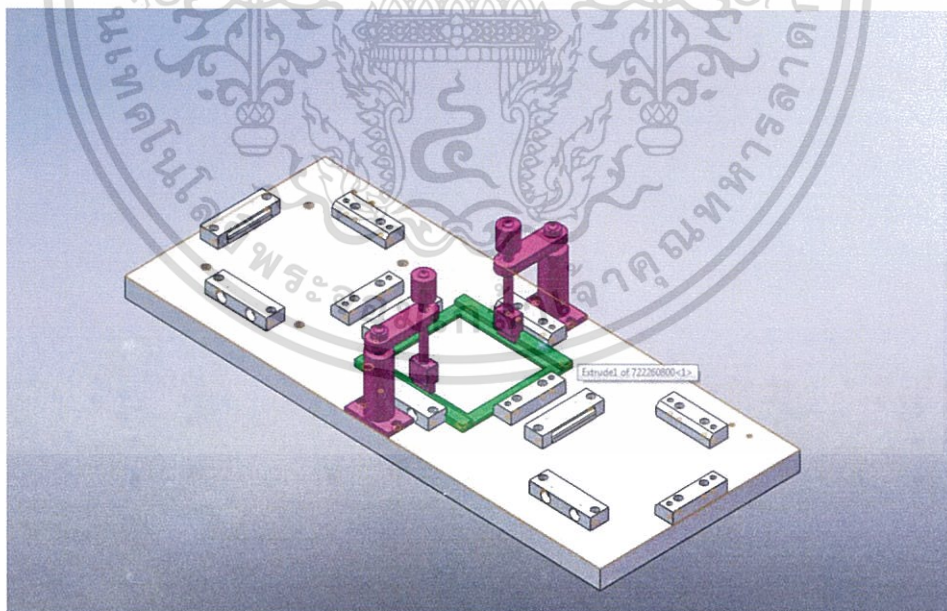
(แสดงรูปตัวอย่าง Drawing B)
